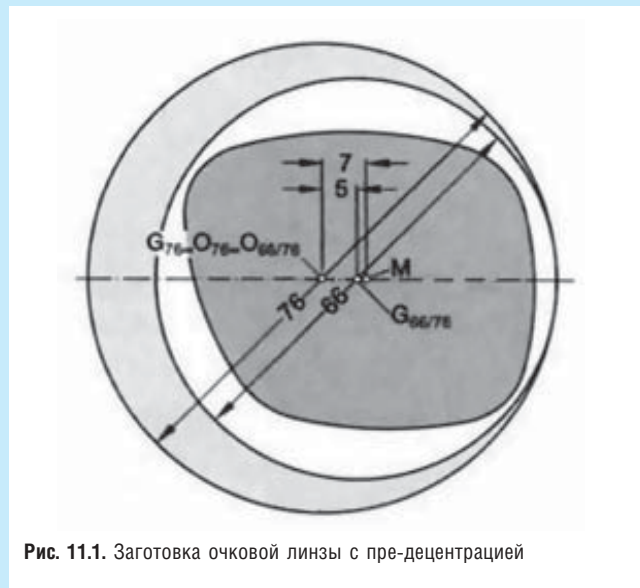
Заготовка очковой линзы с пре-децентрацией
